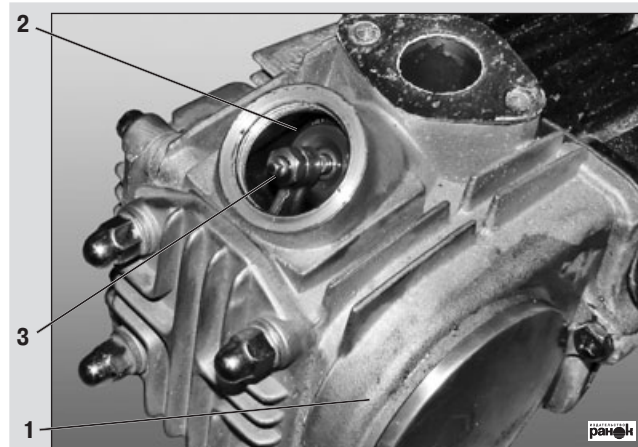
Расположение регулировочного винта зазоров клапанов: 1 – головка цилиндра; 2 – регулировочное отверстие; 3 – регулировочный винт
